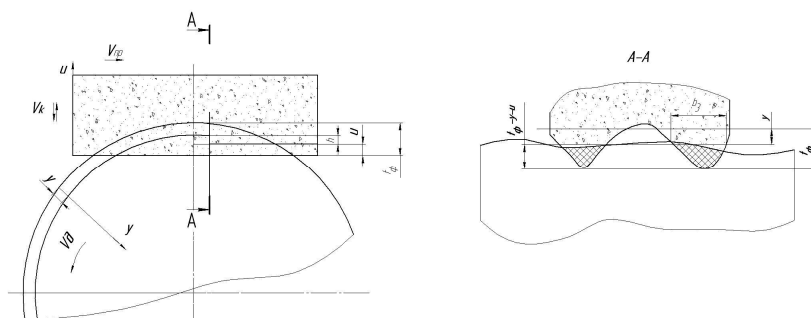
Схема процесса суперфиниширования для расчета вероятности съема материала в зоне контакта заготовки с инструментом
